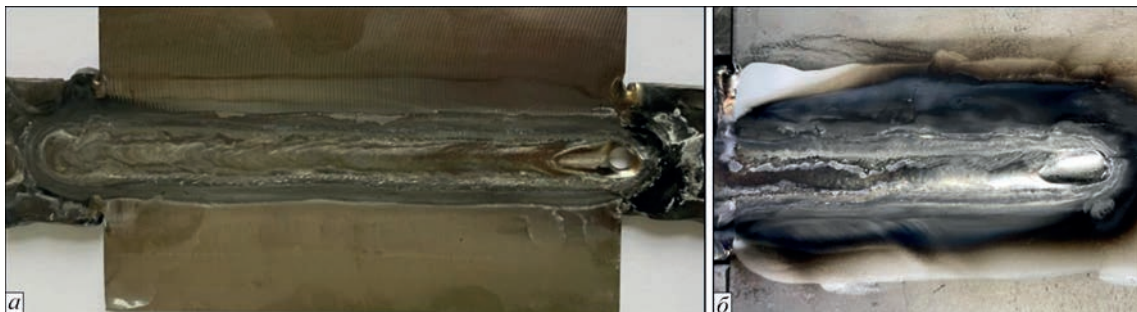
Приклад зварного з’єднання жароміцного титанового сплаву Ti-6,5Al-5,3Zr-2,2Sn-0,6Mo-0,5Nb-0,75Si, виконаного А-ТІГ зварюванням: а – лицьова сторона; б – зразок в печі після зварювання
